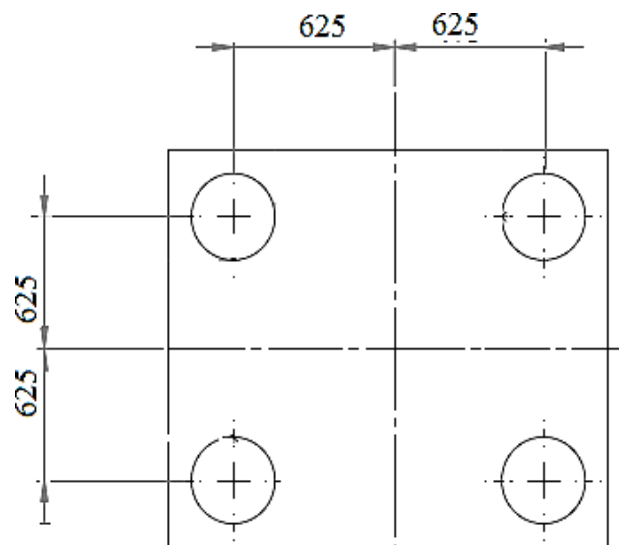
Schéma d'un plateau d'une presse 650T [14].
